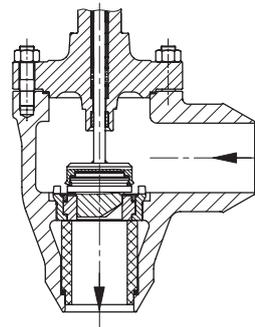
Клапан Тип 3256 с керамическими деталями корпуса и износостойкой керамической трубой
